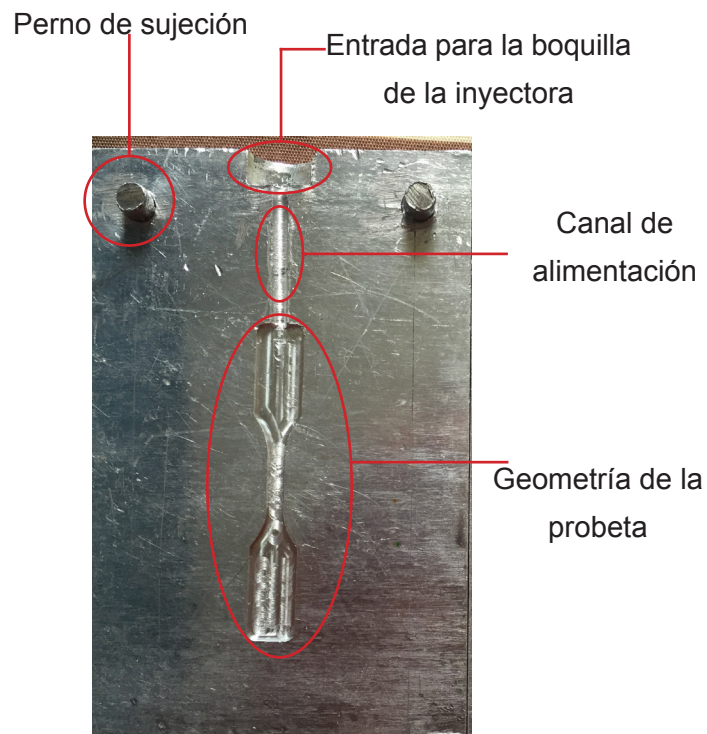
Cavidades del molde utilizado en la inyección de probetas, así como las partes que lo conforman.
